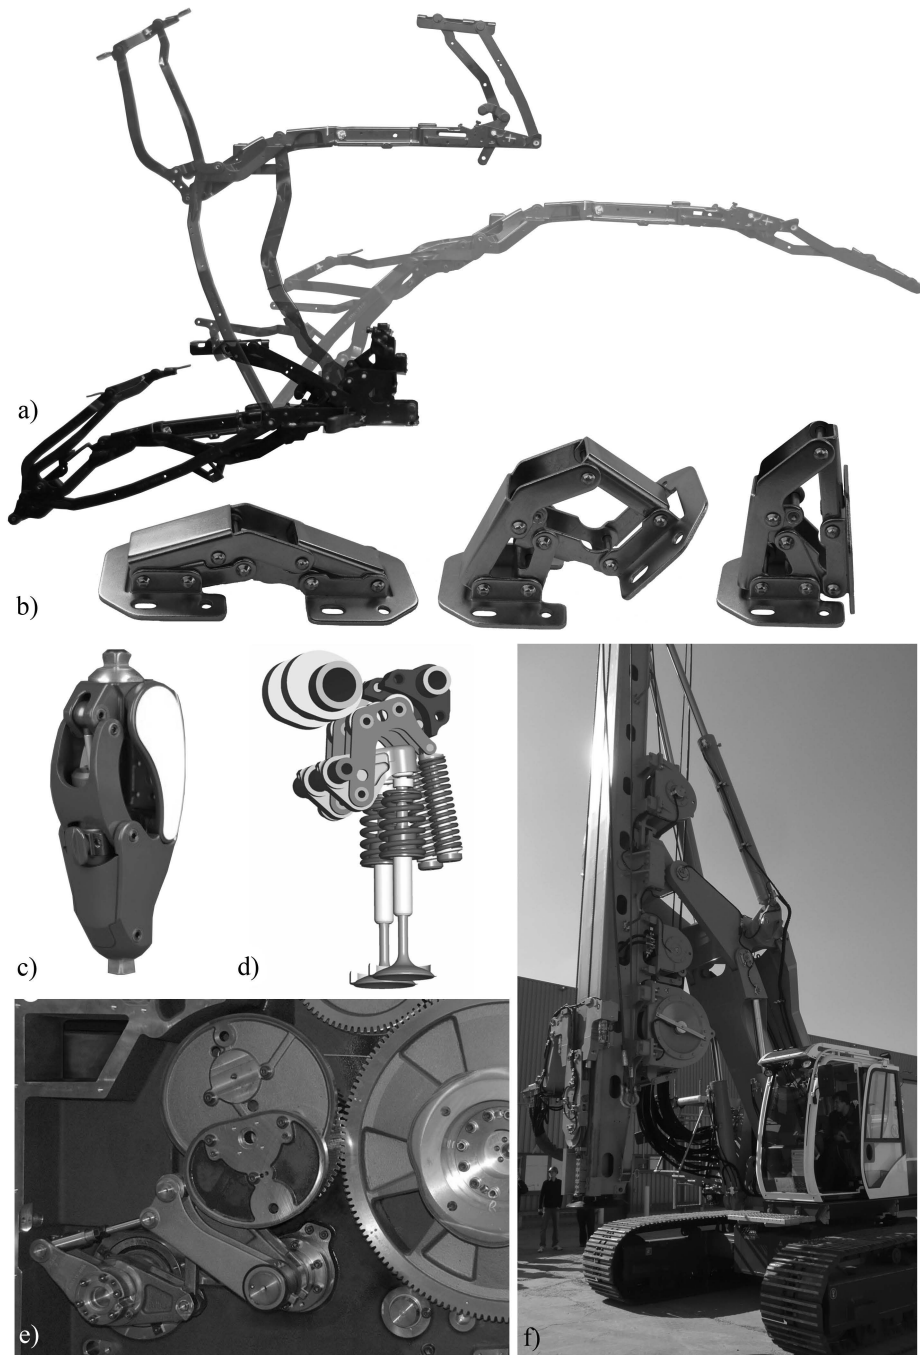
b zeigt ein Scharnier für eine Möbeltür. Der mehrgliedrige Aufbau erlaubt ein Öffnen des Türblattes ohne Kollisionen mit dem Korpus und schränkt zudem den Öffnungswinkel stabil ein.
